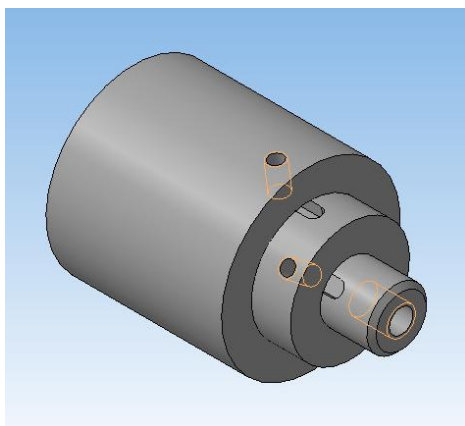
3D-модель сборочной единицы, состоящей из цилиндров
